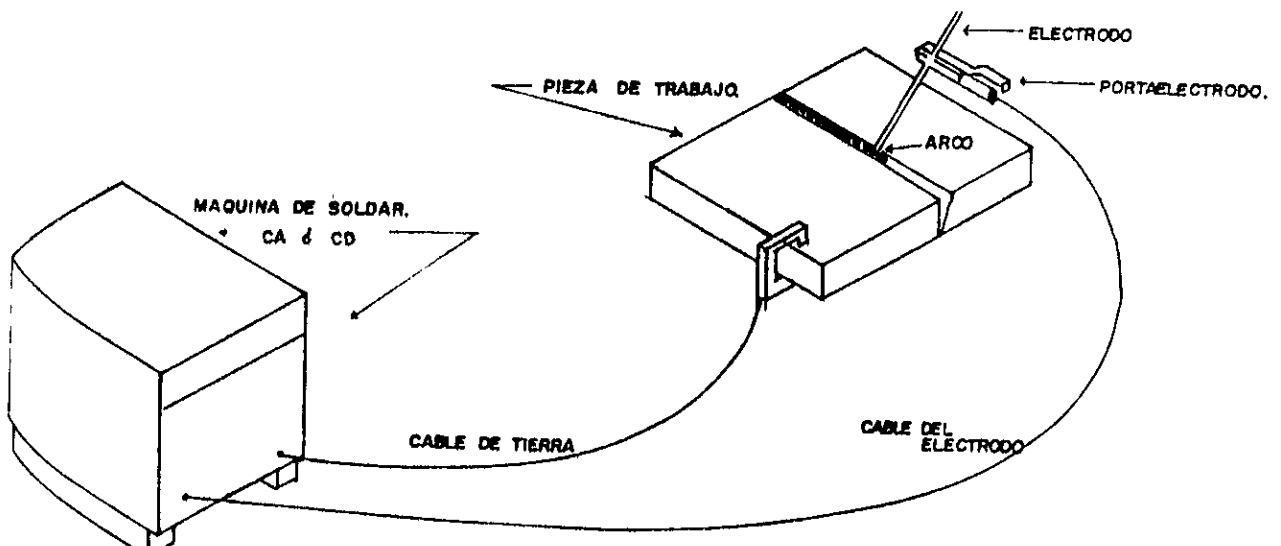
Disposición de elementos básicos para soldadura de arco eléctrico.
